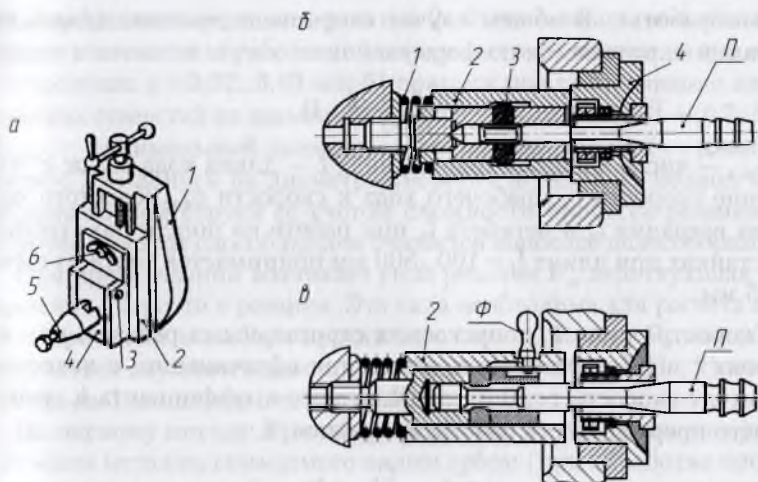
Приспособления для закрепления инструментов на строгальных и протяжных станках:
